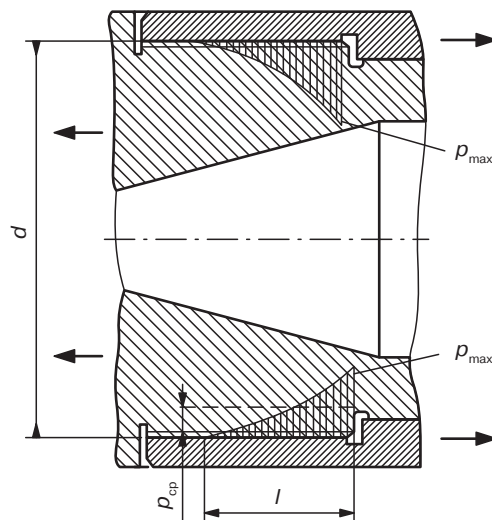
Схема резьбового соединения сопла и материального цилиндра
